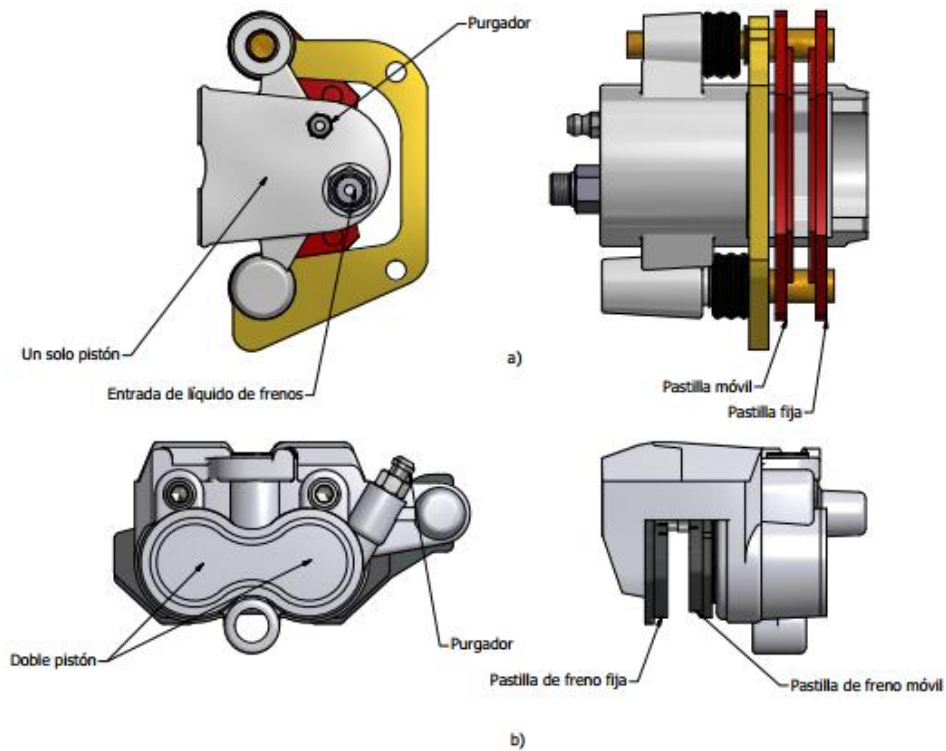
Componentes de: a) Caliper de montaje flotante de un pistón. b) Caliper de montaje flotante de doble pistón.
